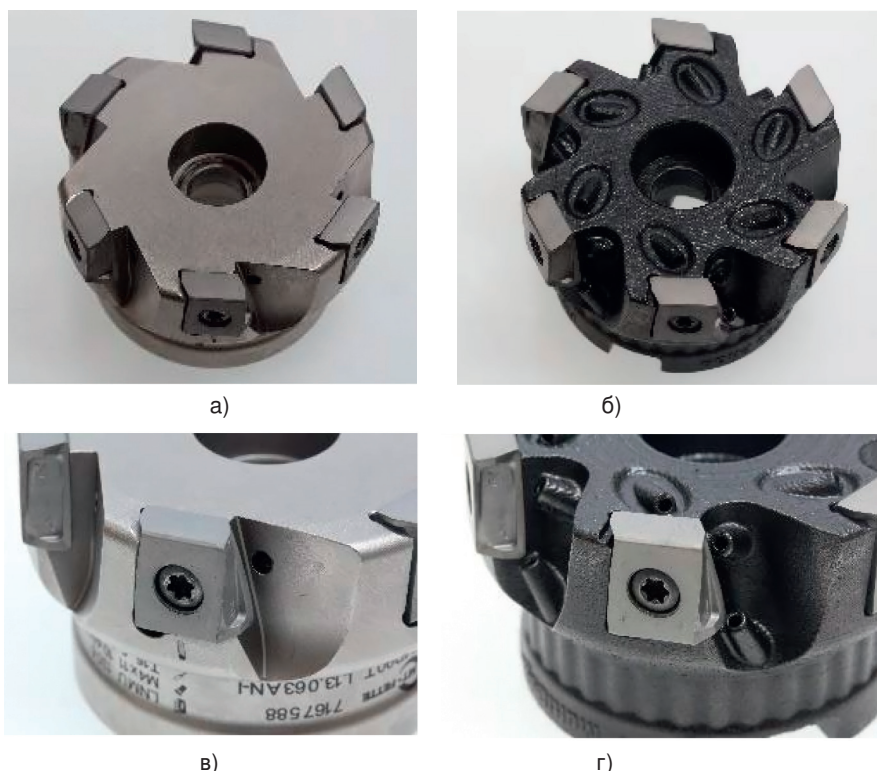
Конструкция корпусной фрезы: а, в) традиционное изготовление; б, г) с применением аддитивных технологий
